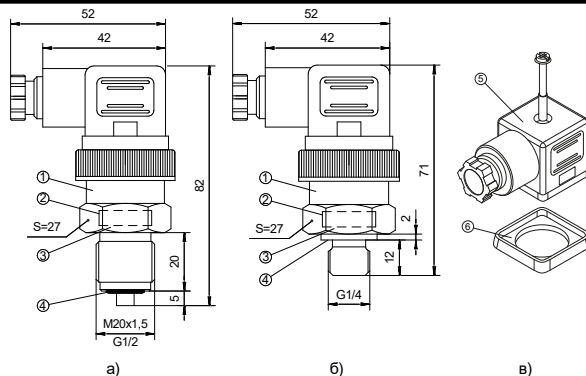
Габаритные размеры и состав конструкции датчика:
